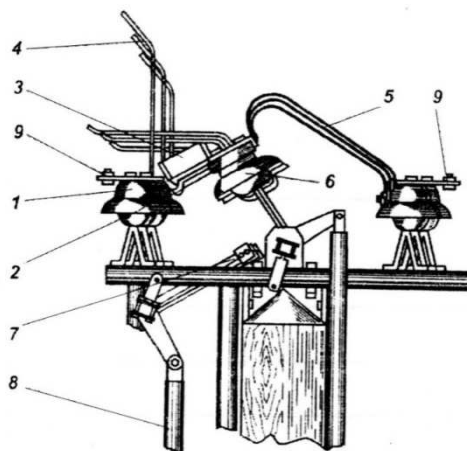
Трёхполюсные разъединители качающего типа наружной установки на 10 кВ с заземляющими ножами:
